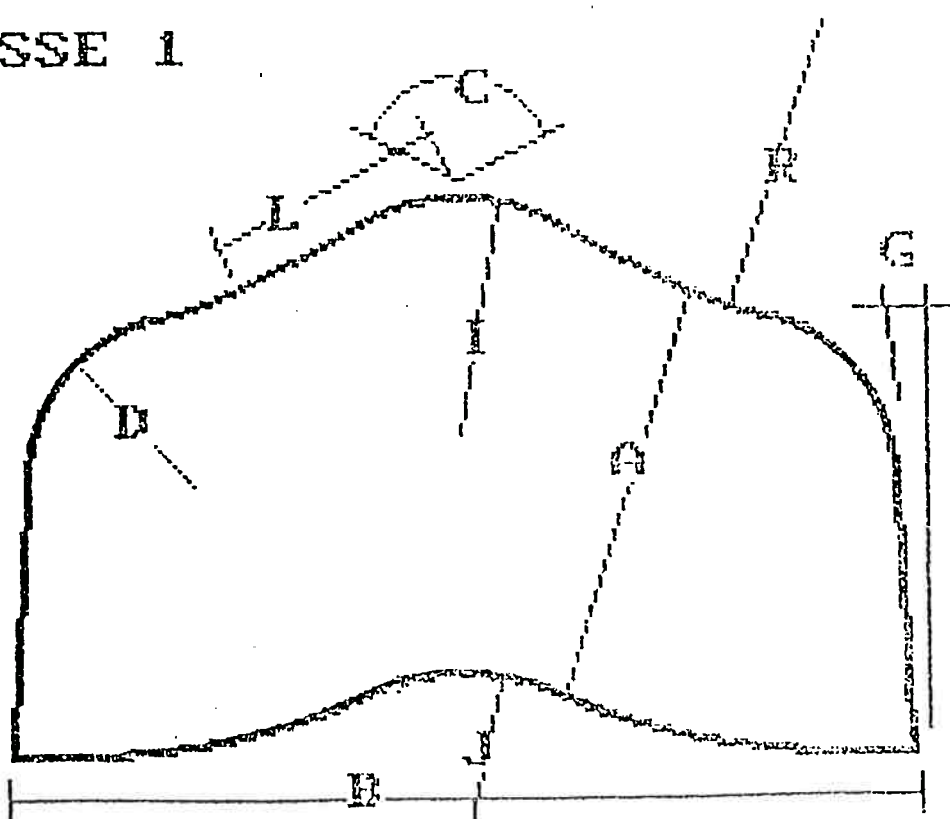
b - Desenho esquemático do primeiro passe de laminação
